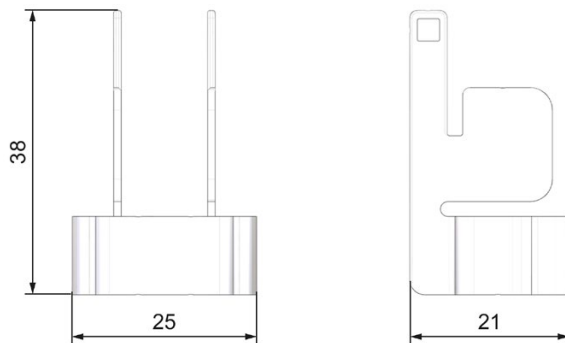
Maßbild Schirmbügel für 25 mm-Module
